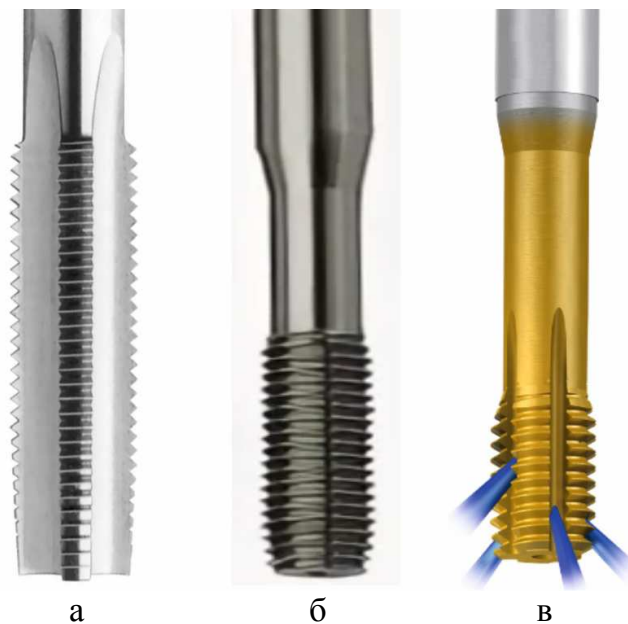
Инструменты для получения внутренней резьбы: а – метчик для нарезания резьбы, б – метчик для накатывания резьбы, в – метчик для накатывания резьбы со смазочными канавками и каналами под СОТС
